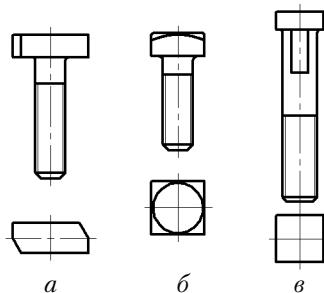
Болты пазовые для крепления станочных приспособлений:
